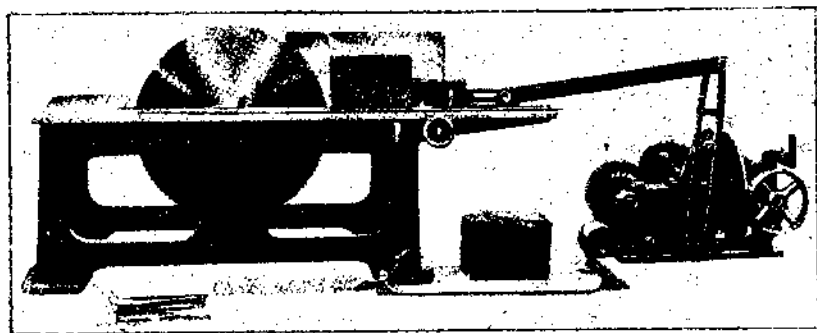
Пильный станок с автоматической подачей дерева фирмы W. & L. Cole
